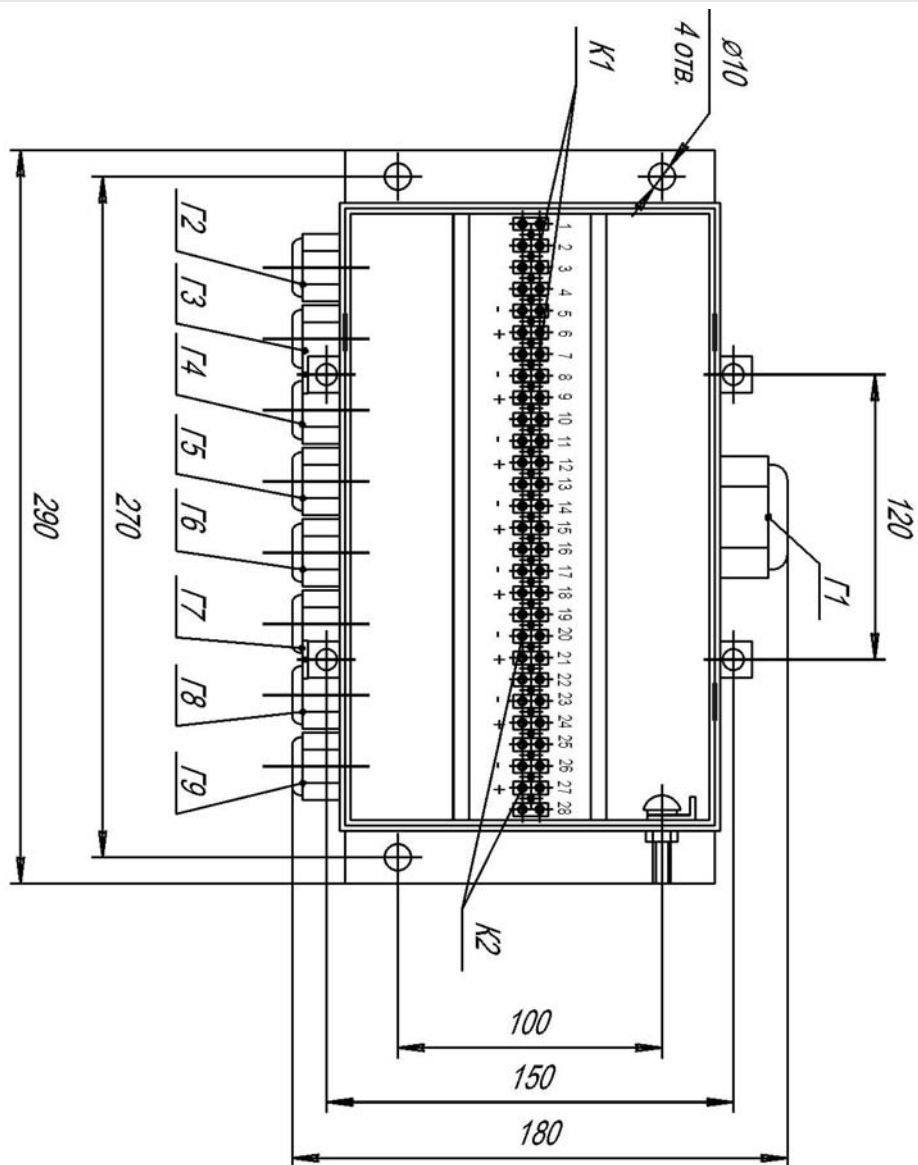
Монтажный чертеж и габаритные размеры БС
